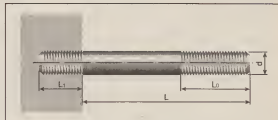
Основные размеры простой шпильки: L_1 – длина резьбы ввертываемого конца; L – длина выступающей части; L_2 – длина резьбы свободного конца; d – резьба шпильки.
